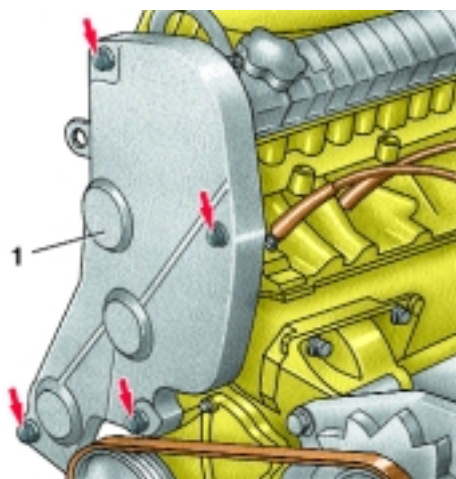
Крепление переднего кожуха ремня привода ГРМ двигателя мод. F3R 272: 1 – передний кожух ремня привода ГРМ
